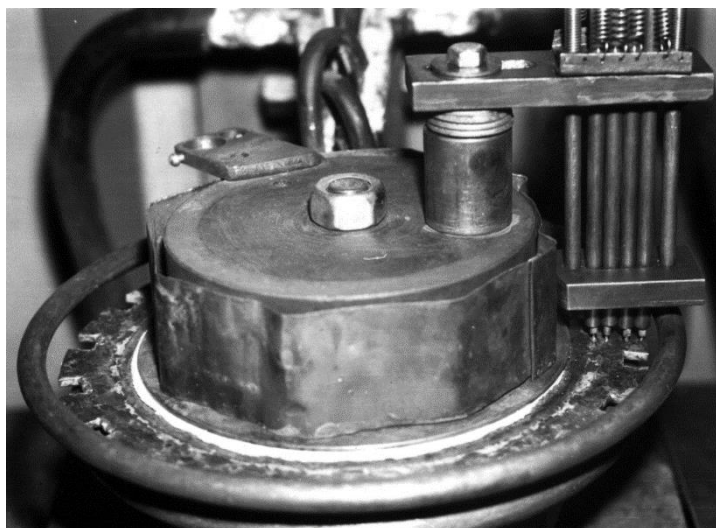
Пристосування для встановлення деталі в кільцевому двохвитковому індукторі
